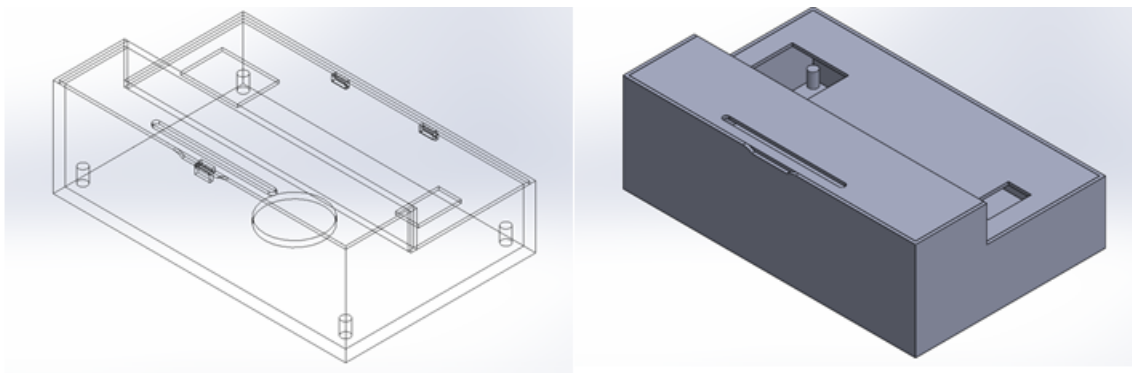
Desenho CAD 3D em SOLIDWORKS.
